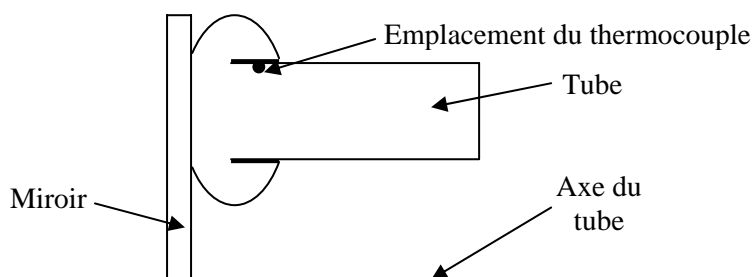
Position en fin de soudage du thermocouple placé initialement à 5 mm du plan de soudage à 1 mm sous la surface du tube. Le thermocouple est recouvert par le bourrelet
